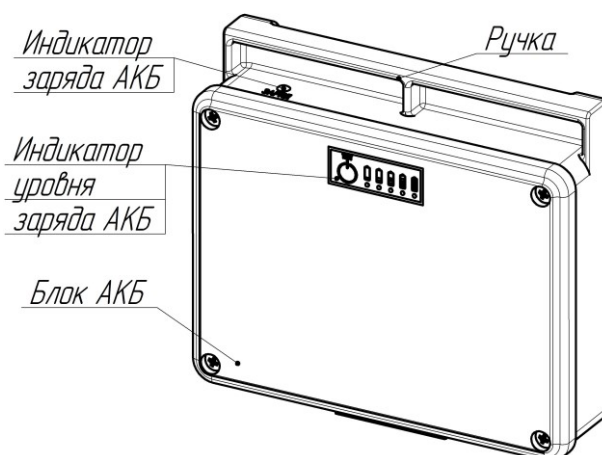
Внешний вид блока АКБ (вид сверху)
